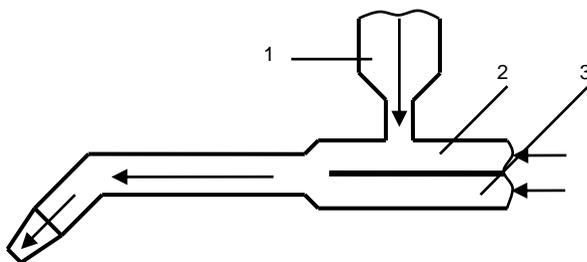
Схема горелки для газопорошковой наплавки:
